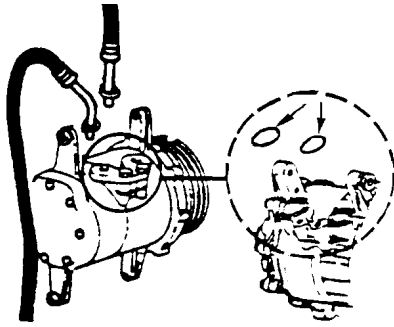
Austausch der alten R12 O-Ringe gegen neue R134a O-Ringe
